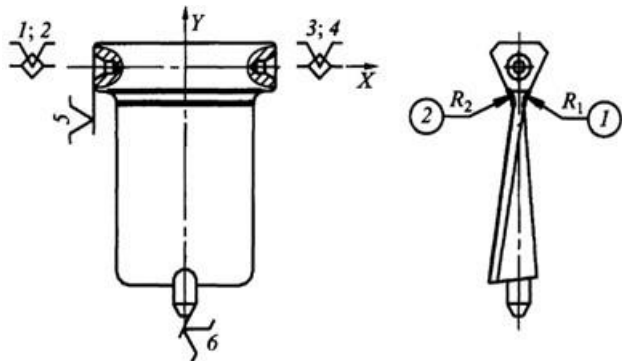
схема базування лопатки під час обробки радіусів R_1 й R_2 переходу з боку спинки й корита.
